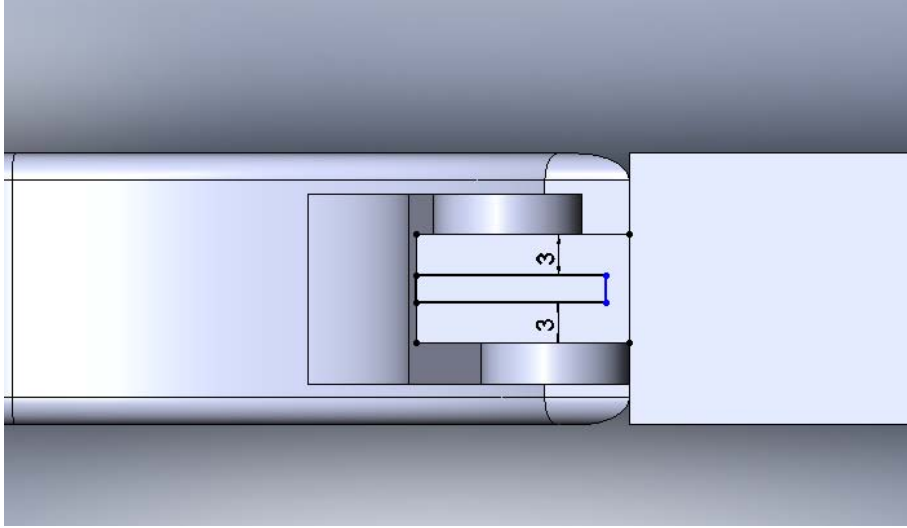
İkinci yüzey 2. 3D milling işlemi
